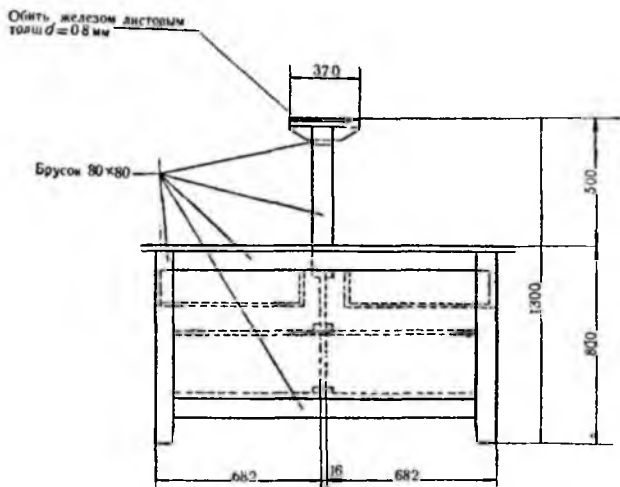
Двусторонний верстак для ремонта шатуно-поршневой группы (вид с торца).
